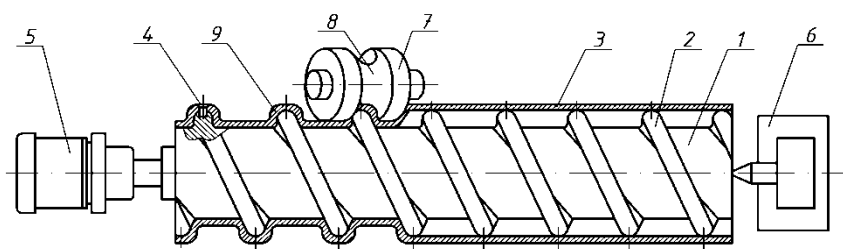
Конструктивна схема способу виготовлення U-подібної гвинтової поверхні транспортної труби
